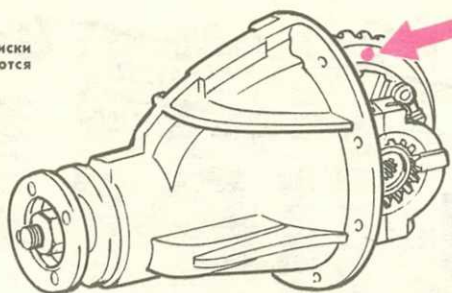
Модель и количество зубьев шестерен главной передачи выбиты на торце ведомой шестерни.
